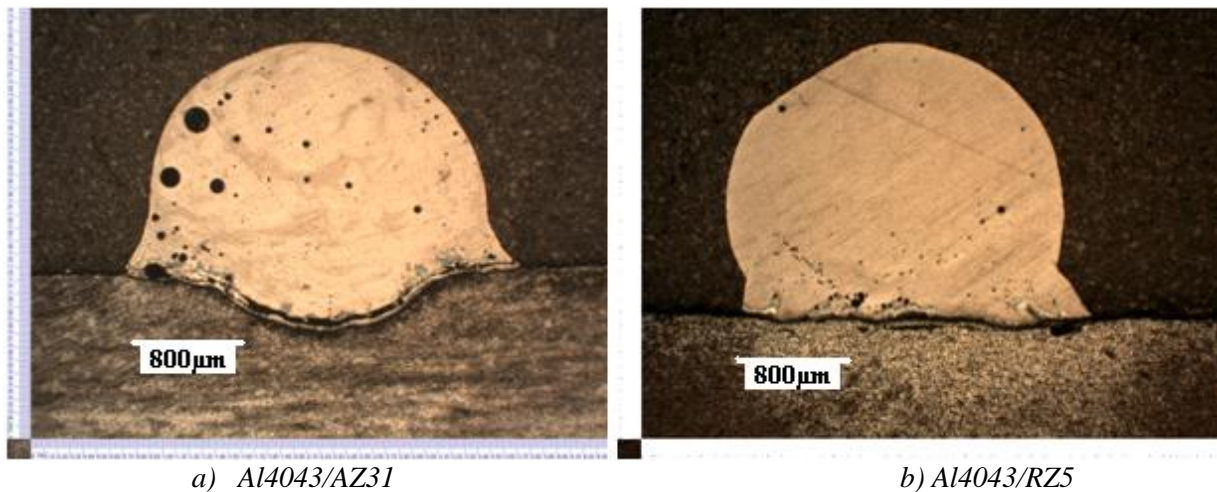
Macrographie de dépôts pour le couple en soudage CMT, $V_s=800$ mm/min, $V_f=3000$ mm/min
